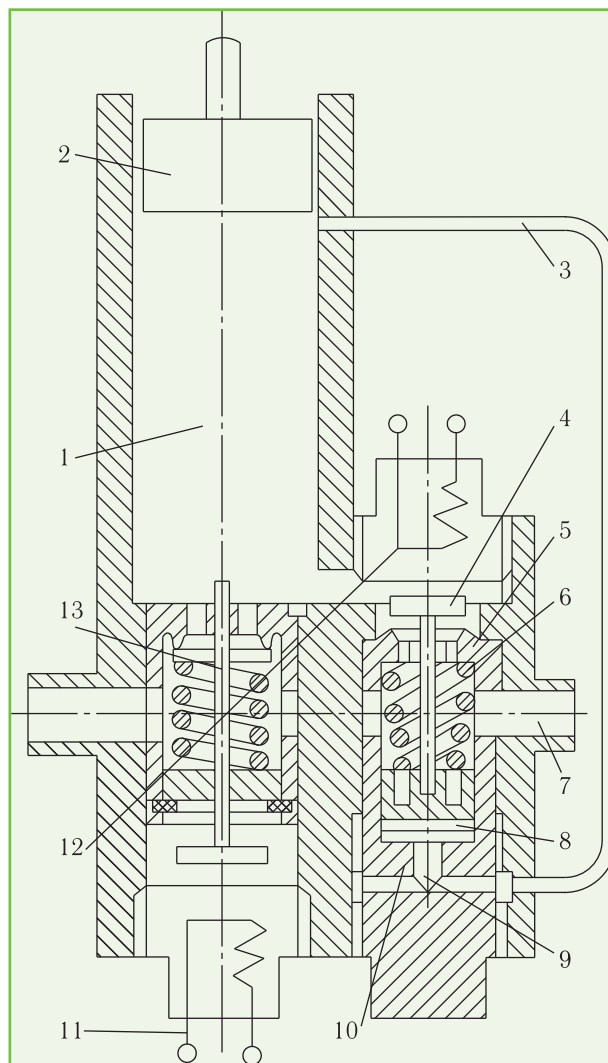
Конструкция электромагнитного привода клапанов поршневого детандера: 1 — цилиндр; 2 — поршень; 3 — импульсная трубка; 4 — выпускной клапан; 5 — седло выпускного клапана; 6 — пружина; 7 — выпускной патрубок; 8 — камера пневмопривода; 9 — канал; 10 — поршень пневмопривода; 11, 12 — электромагниты; 13 — впускной клапан
